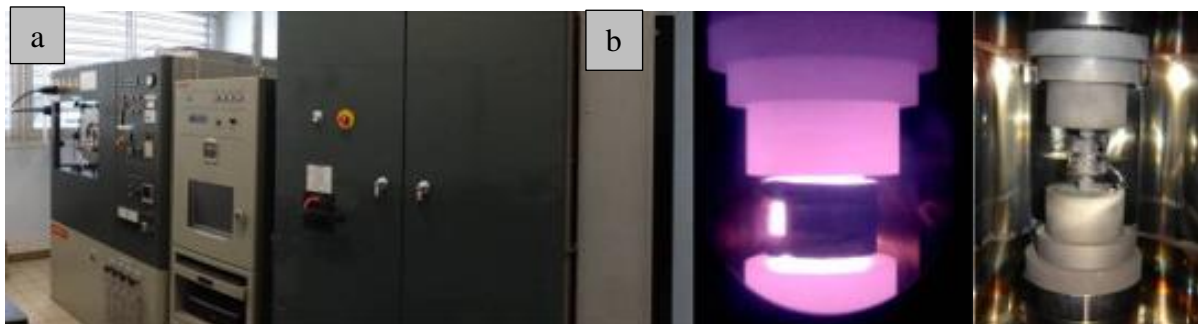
Machine de frittage SPS 2080 Fuji; a) vue générale de la machine b) mise en position matrice/pistons
